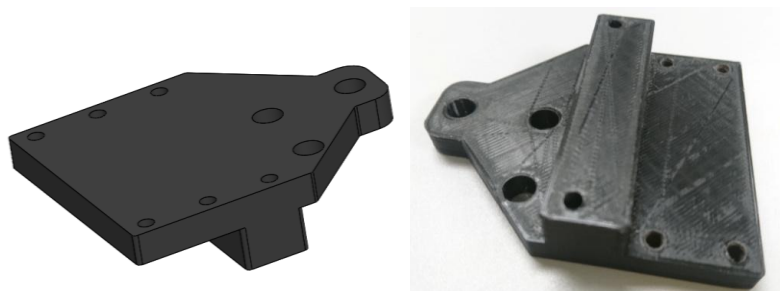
Modelo CAD y pieza final impresa del soporte del extrusor.
